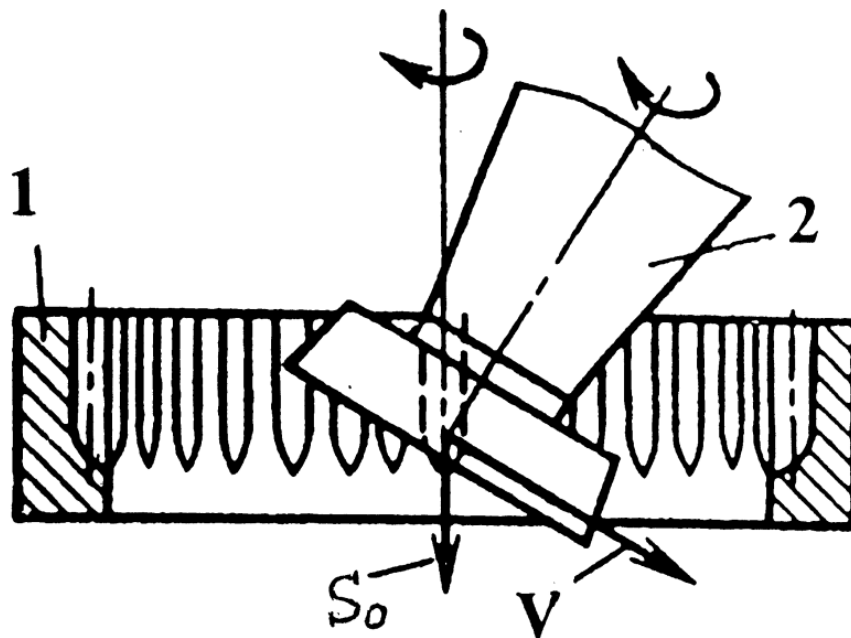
Процесс создания зубчатых колес методом зуботочения .
